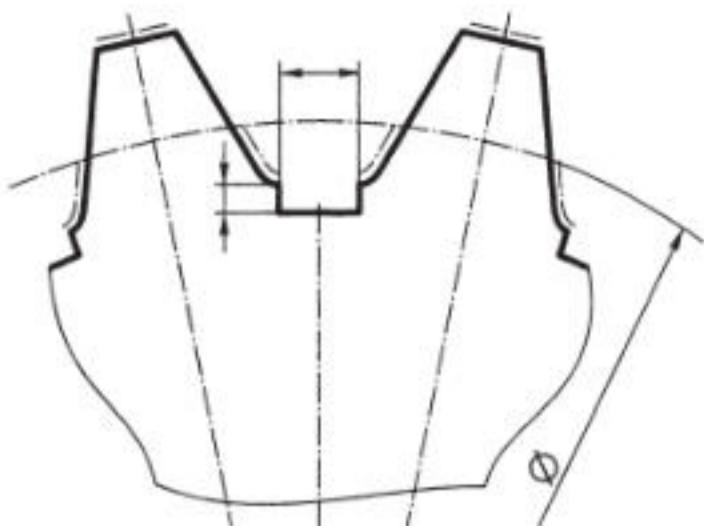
Пример изображения профиля звездочки для пластинчатых цепей с нестандартизированными участками
